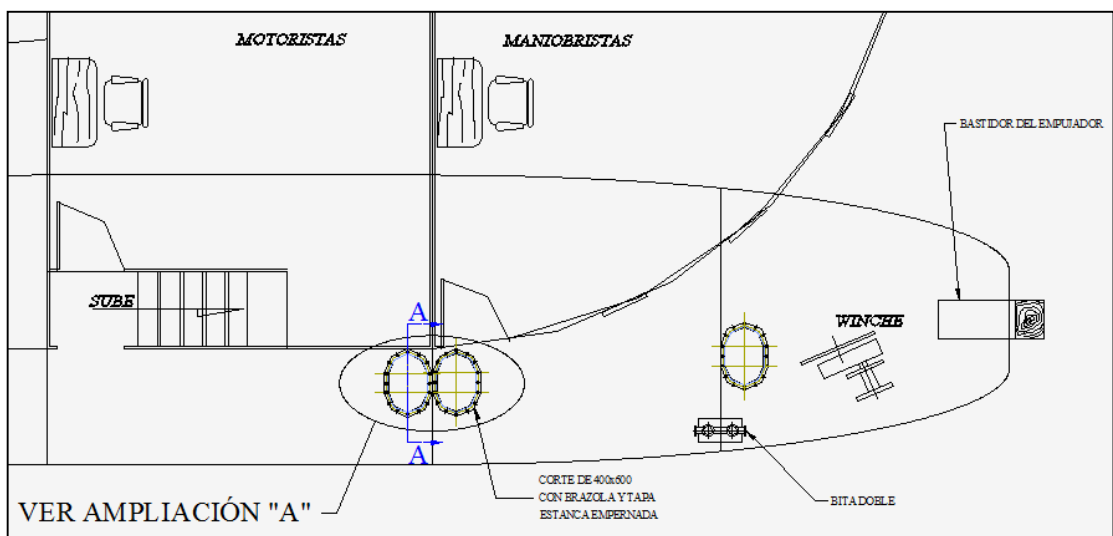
Vista de planta lado de estribor, ubicación de tapas de registro en la zona de proa a partir de la sección media.
